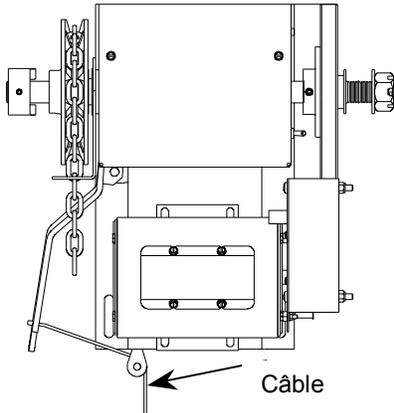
Installation du câble sur l'ouvre-porte MSJ
